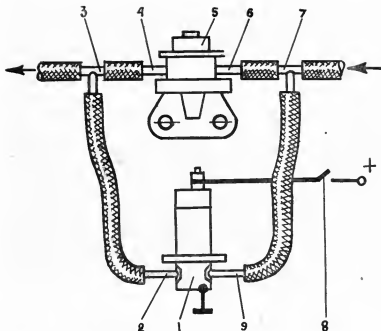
Подключение дополнительного электромагнитного насоса: 1 — дополнительный насос; 2 — нагнетательный патрубок дополнительного насоса; 3, 7 — тройники; 4 — нагнетательный патрубок основного насоса; 5 — основной насос; 6 — всасывающий патрубок основного насоса; 8 — включатель; 9 — всасывающий патрубок дополнительного насоса.
